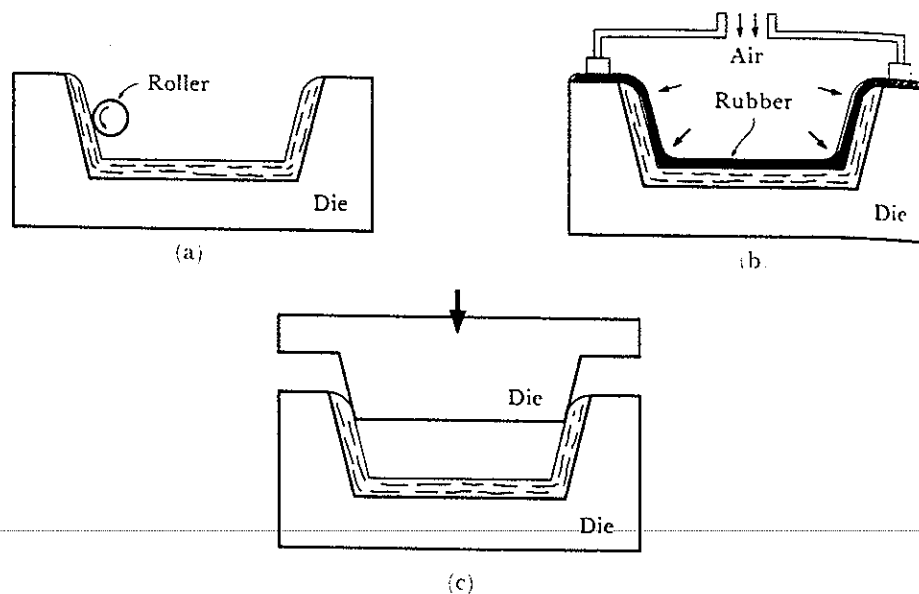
Méthodes de fabrication de composites fibreux dans des moules, (a) hand lay-up, (b) pressure bag molding at (c) matched die molding.
